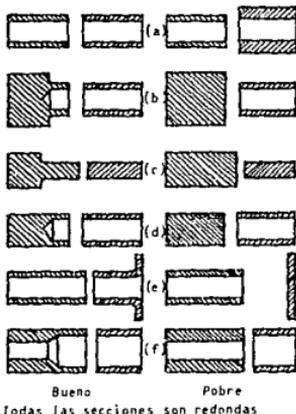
Ejemplos de diseño bueno y pobre de unión para obtener balance de calor entre las piezas en la soldadura por arco con presión.
